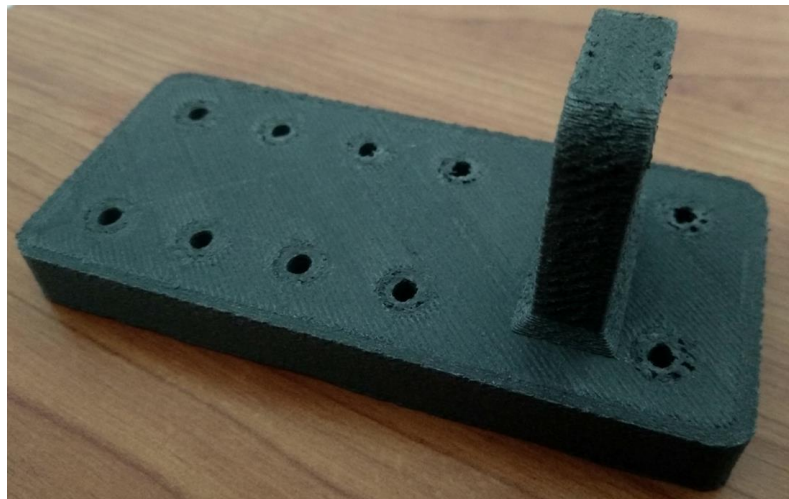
Impressão 3D Placa Bidirecional (b)
